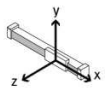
Izbor parametara koji se odnose na motor i motor kontroler električne ose
